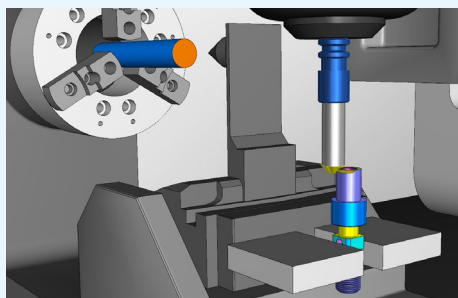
Станки типа «bar-fed milling machine» позволяют заменить токарную обработку фрезерованием.
